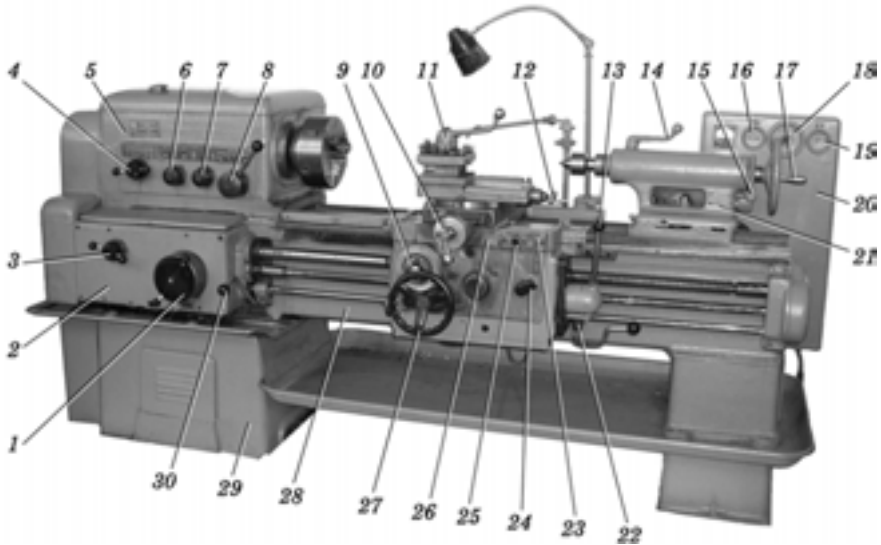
Загальний вигляд токарно-гвинторізного верстата 1К62
